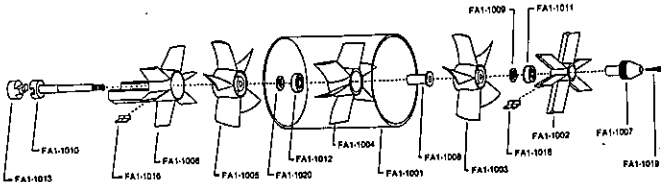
Montagezeichnung des Force Air I Impellers.
